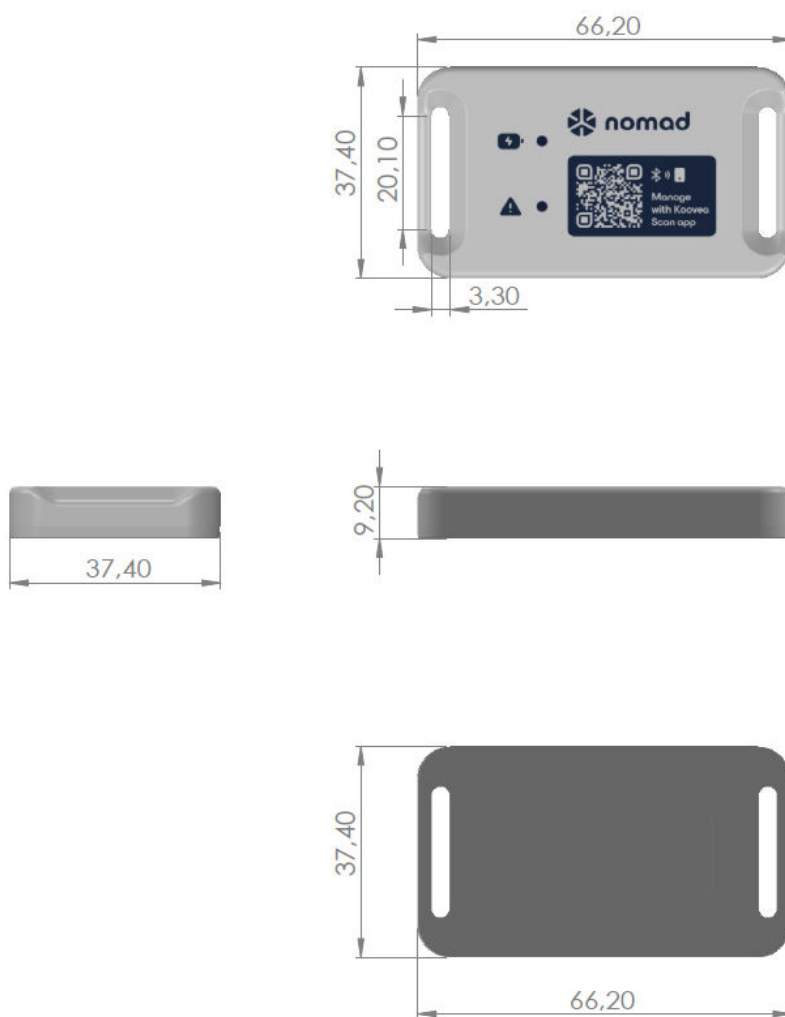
plan mécanique en mm (tolérance ± 2 mm)
